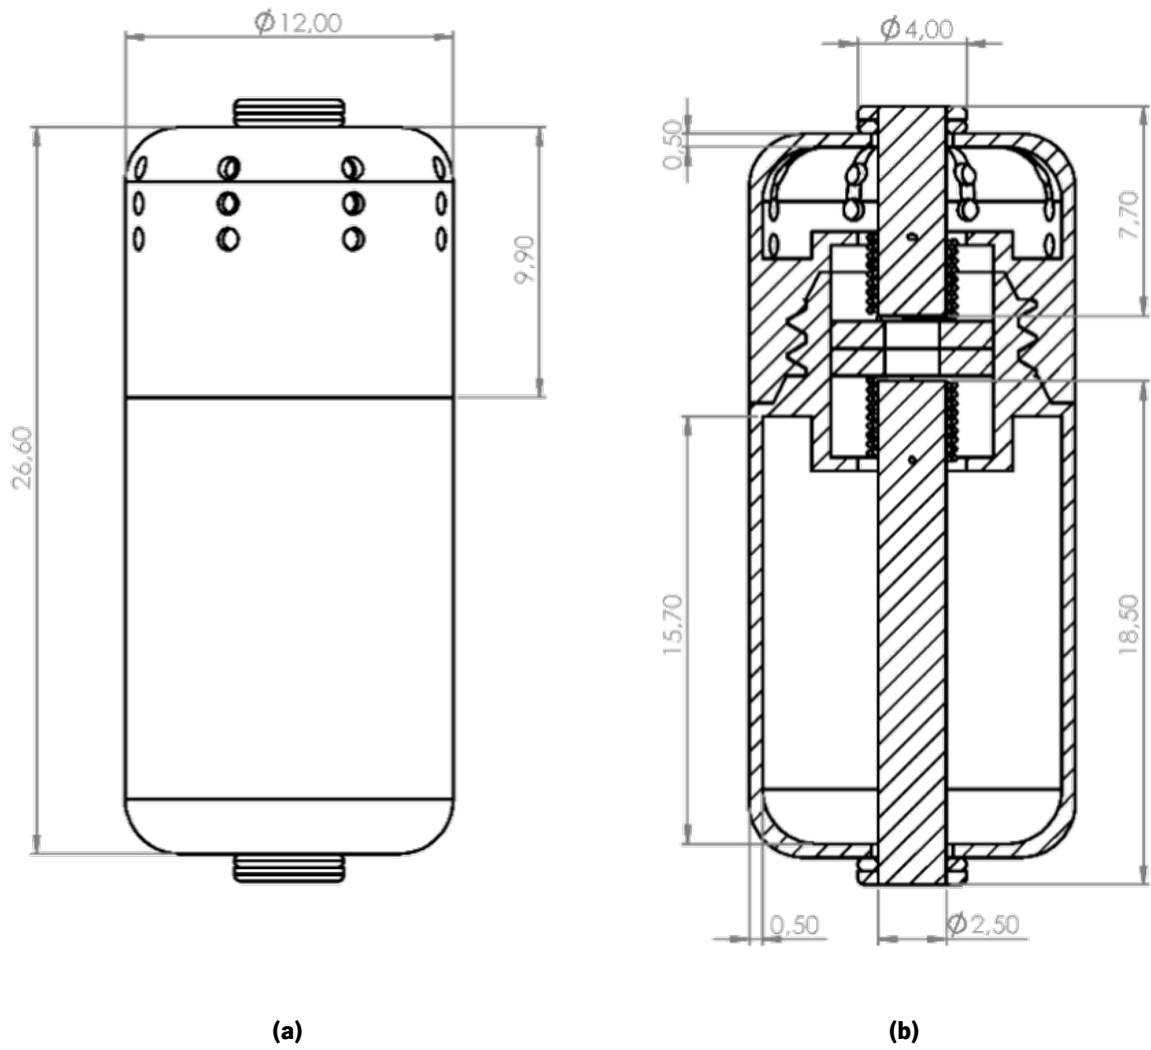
Design* CAD e dimensões (mm) do corpo da cápsula ingerível 2.0: a) vista lateral, b) vista em corte.
